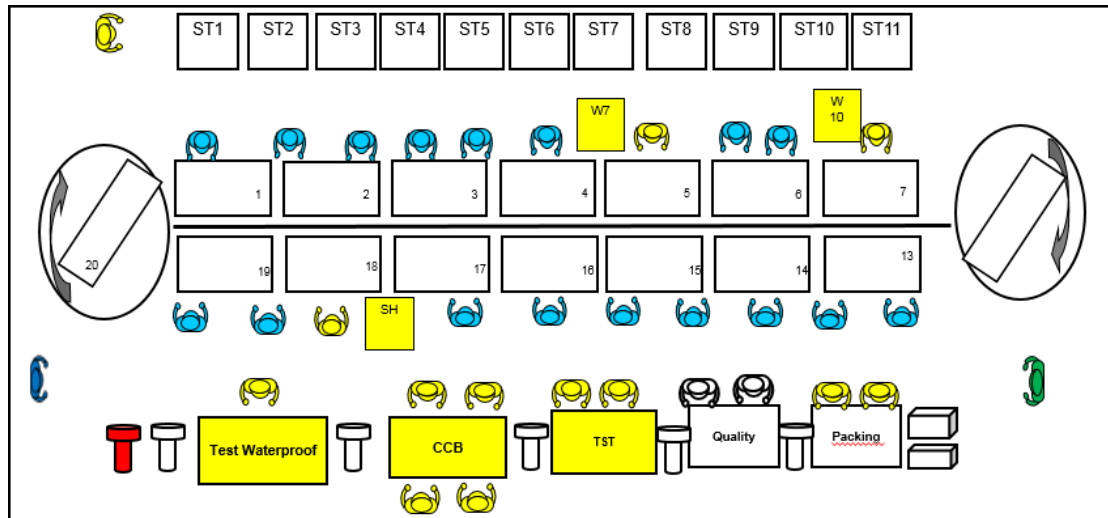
Vue d'ensemble d'une chaîne d'assemblage.
